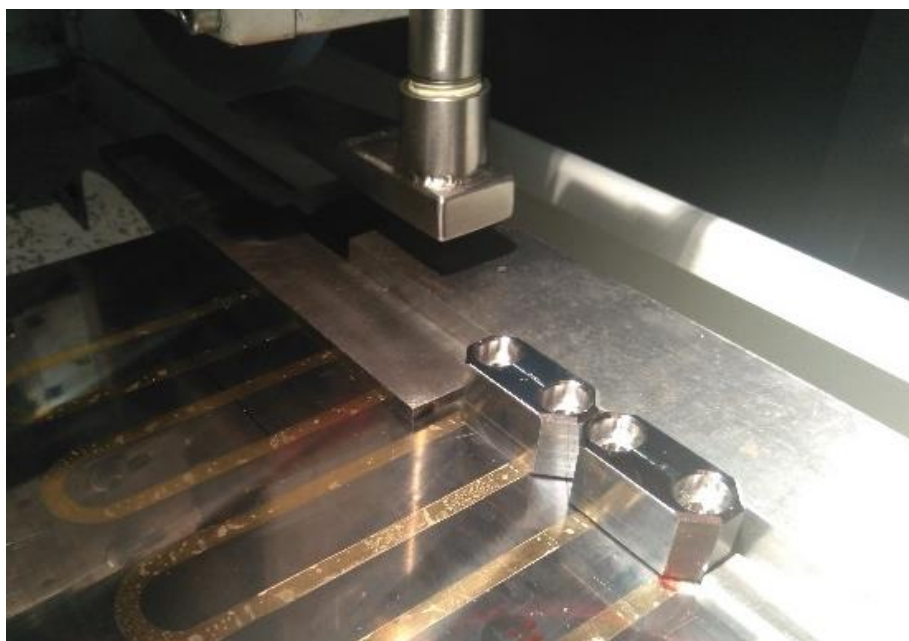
Upnutí součásti ve druhé frézovací operaci
